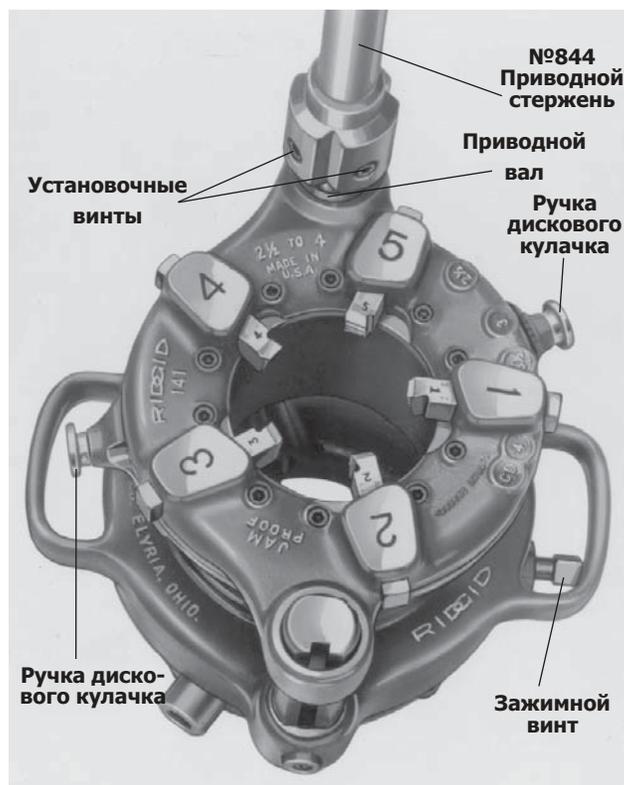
Головка №141 с установленным приводным стержнем №844
